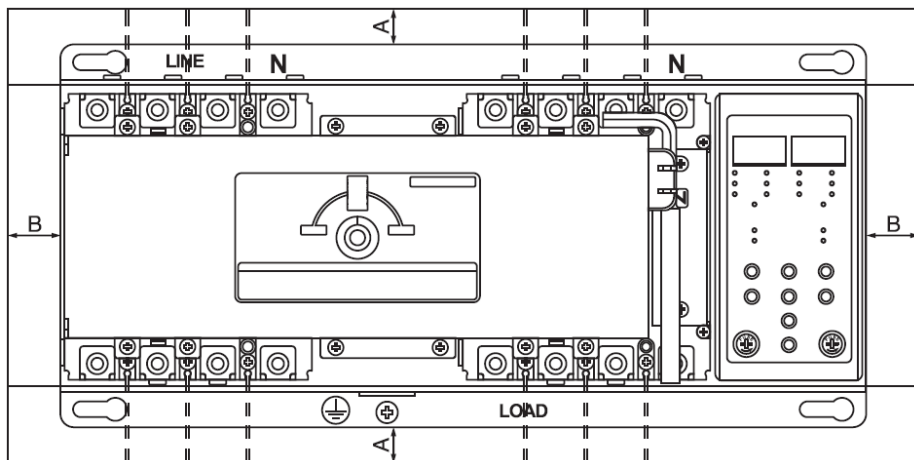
Габаритные размеры АВР-300 400-630А/ЗР, 4Р в цельном корпусе
